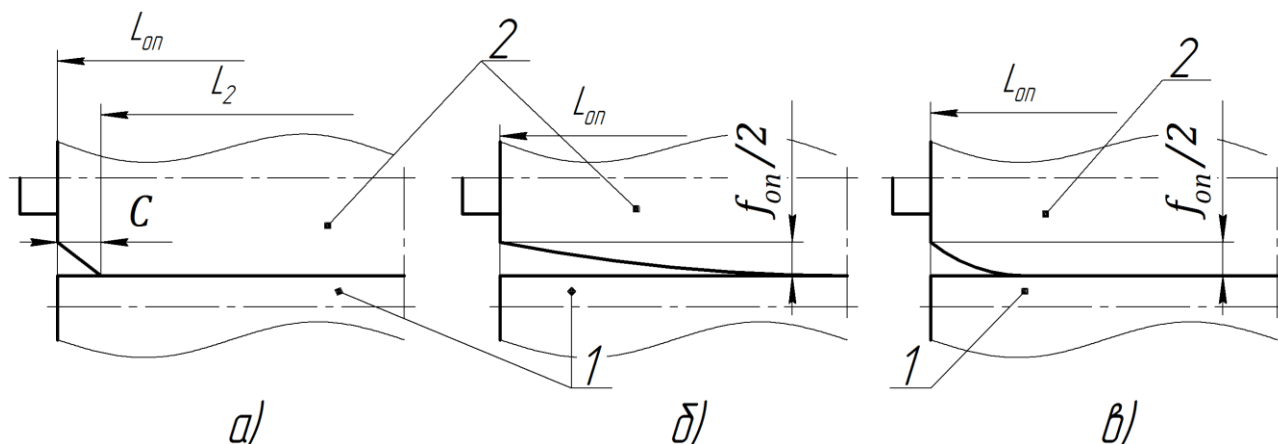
Варіанти профілювання бочки опорного валка : а - циліндричний профіль з крайовим скосом C ; б - опуклий параболічний профіль ($m=2$); в - параболічний профіль з $m=4-8$; 1 - робочий валок з циліндричним профілем твірної ; 2 - опорний валок; C - довжина крайового скосу (урізу) (m - показник міри опуклого профілю валка)
